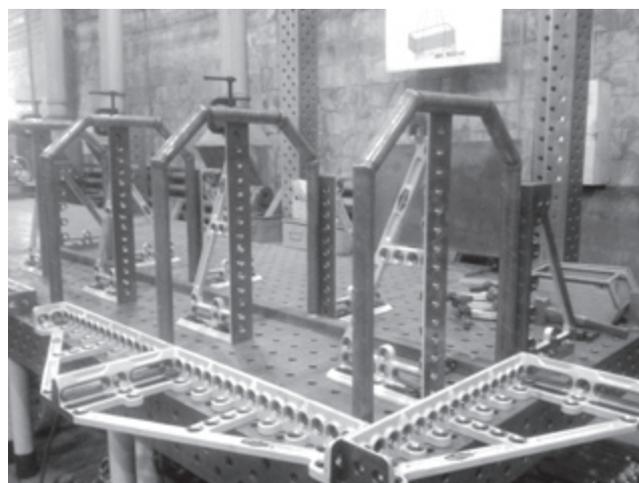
Многофункциональный сборно-разборный сварочный стапель
